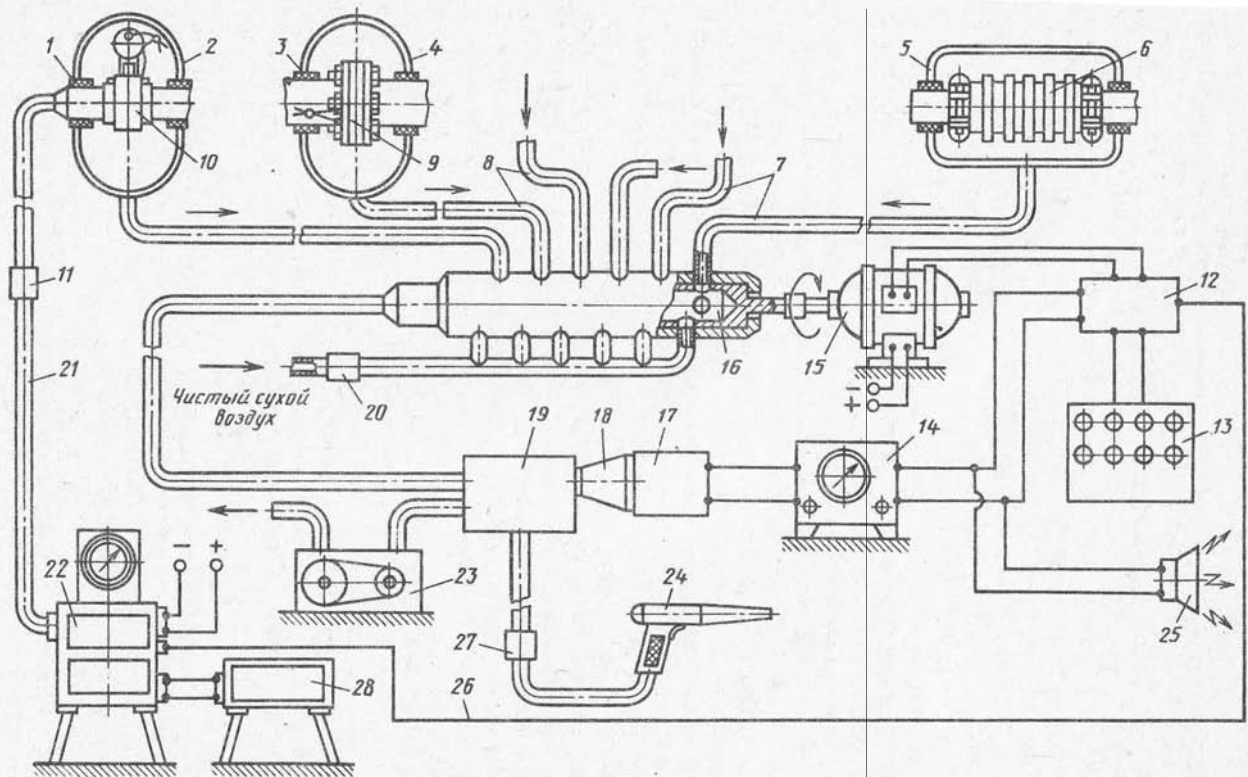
Схема стенда для автоматического контроля герметичности разъемных соединений с помощью инфракрасного газового течеискателя ИГТ-1
